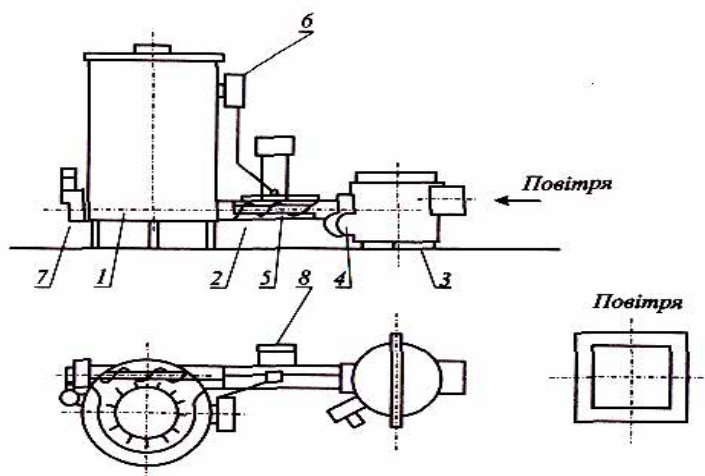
Автоматична установка для спалювання відходів подрібненої деревини AZSO-50: 1 — дозуючий бункер; 2 — шнековий транспортер; 3 — реторта; 4 — нагнітальний вентилятор; 5 — термостатичний вентиль з датчиком; 6 — резервуар з водою для гасіння; 7 — привід транспортера; 8 — система керування
